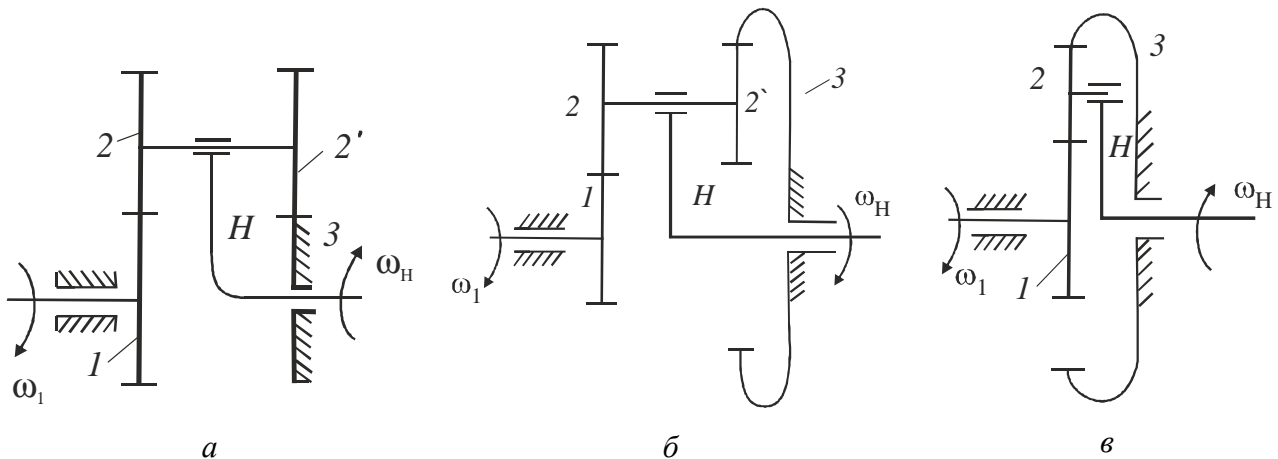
Двухступенчатый планетарный редуктор: a – типа $A-A$; b – типа $A-J$; v – типа $A-J$
